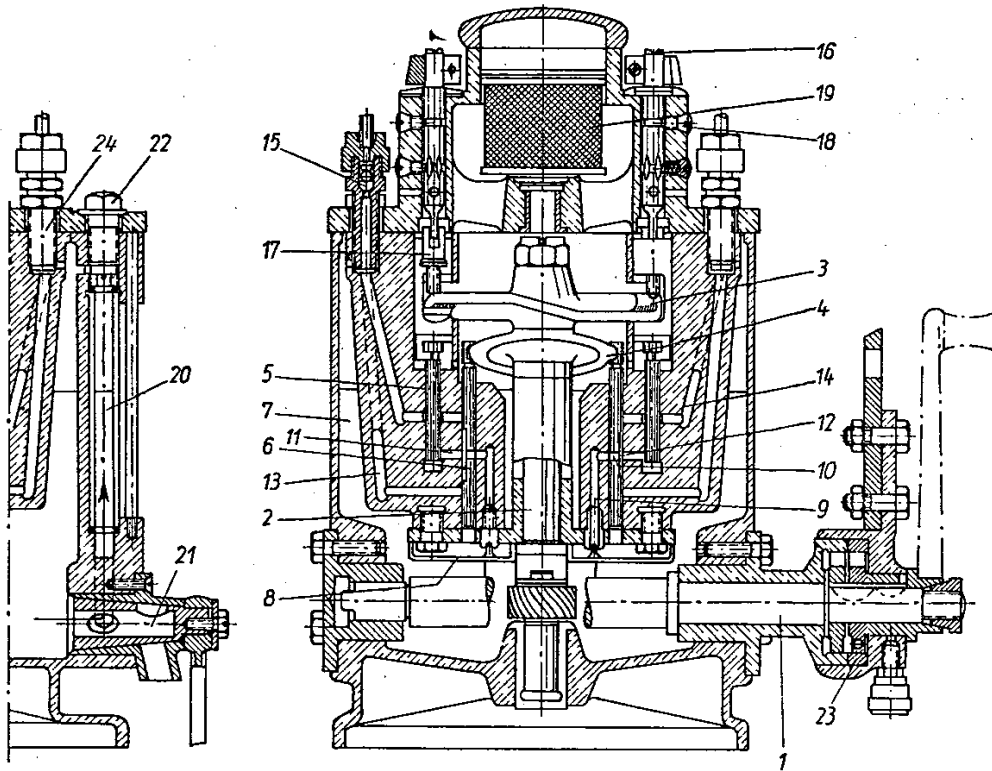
Hochdruckschmierpumpe Bauart Bosch
